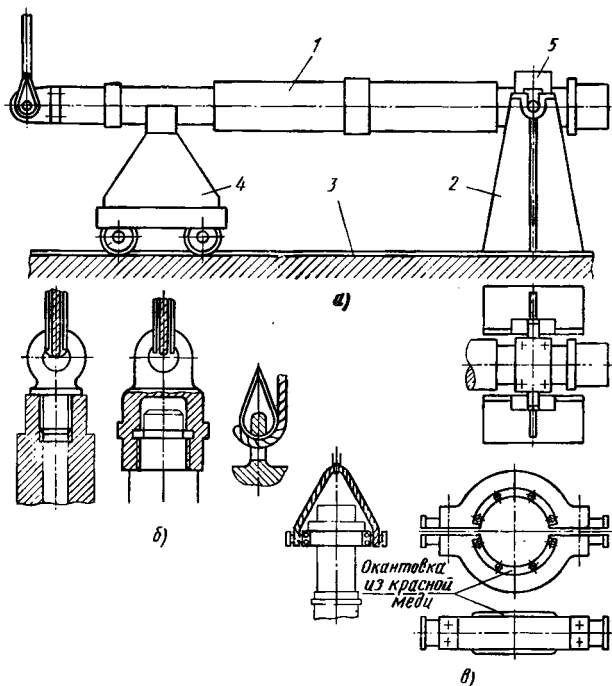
Приспособление для кантовки вала в вертикальное положение:
